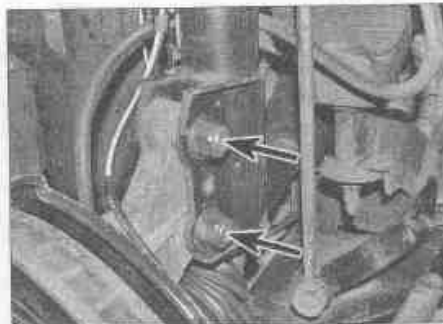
Отпустите гайки крепления стойки подвески к поворотному кулаку
